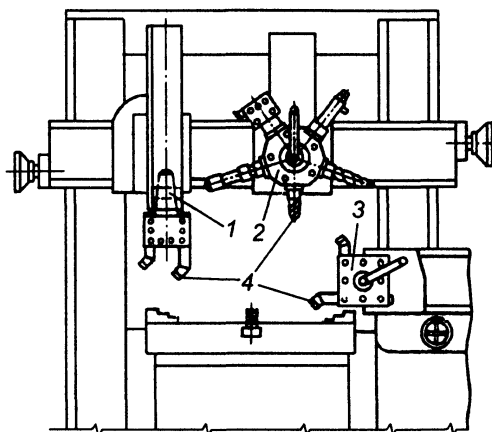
Размещение суппортов и инструмента на токарно-карусельном двухстоечном станке: 1, 2 – вертикальные суппорты; 3 – боковой суппорт; 4 – инструмент
